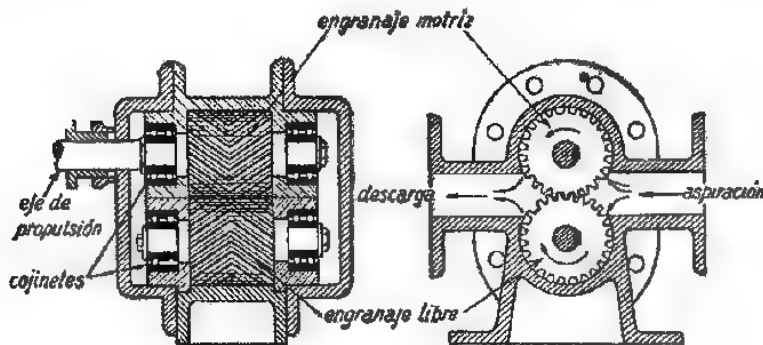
Corte longitudinal y transversal de una bomba de engranajes para aceites lubricantes.
